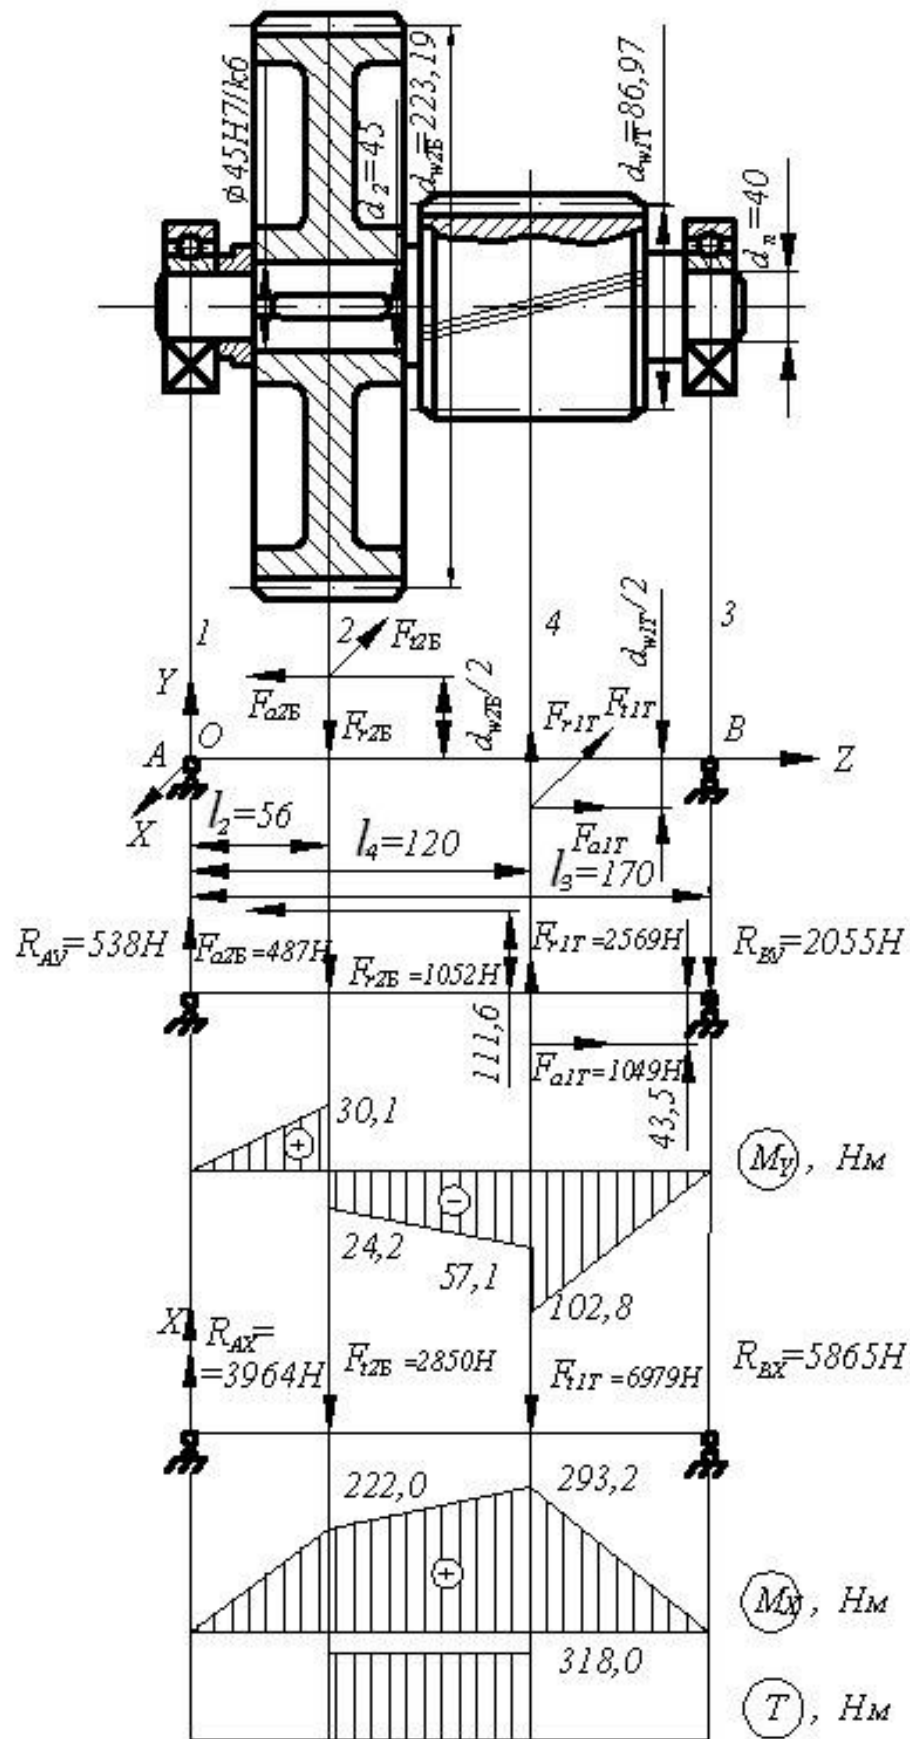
Схема к расчету промежуточного вала цилиндрического двухступенчатого редуктора по развернутой схеме
